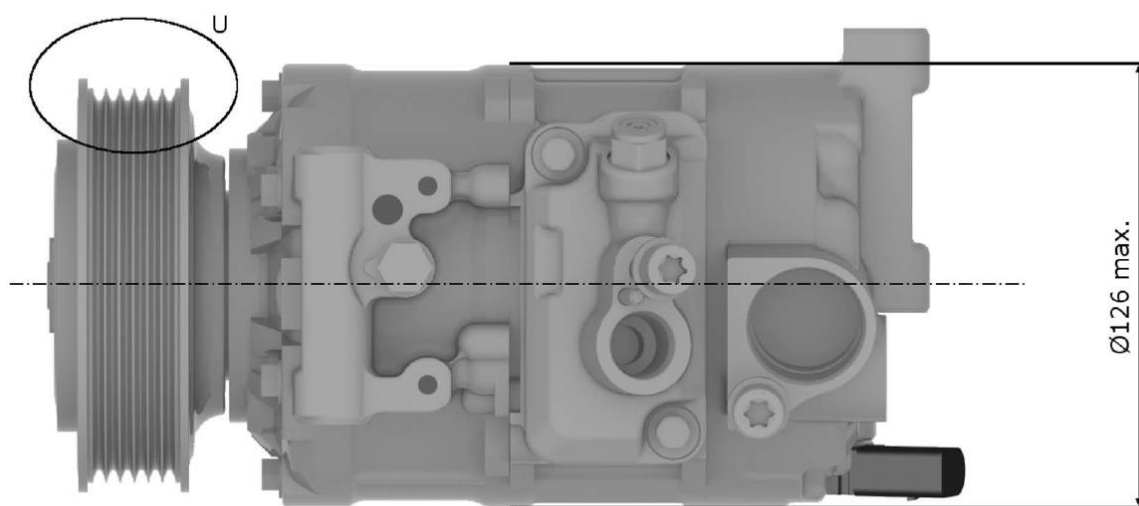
Размеры компрессора климатической установки (вид сверху)
